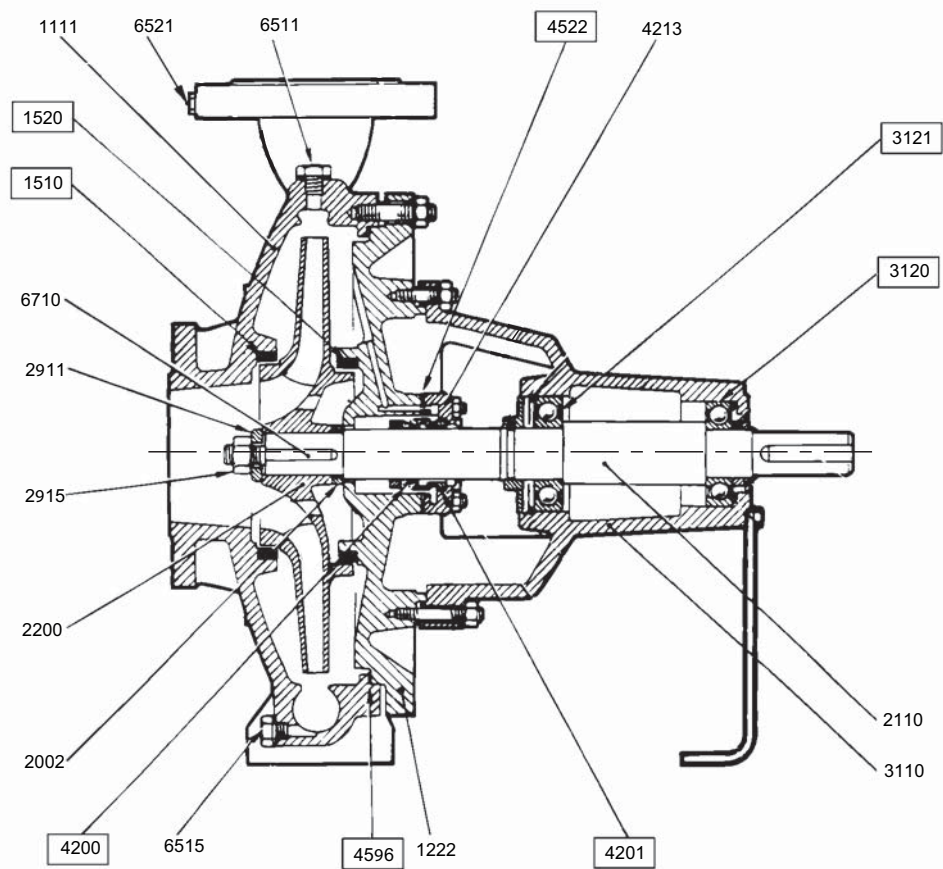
NK 65-315 (2900 мин⁻¹), 65-315 "переразмеренные", 80-315, 80-315 "переразмеренные", 80-400, 100-315, 100-315 "переразмеренные", 100-400, 125-250, 125-250 "переразмеренные", 125-315, 125-400, 250-310 "переразмеренные" насосы
